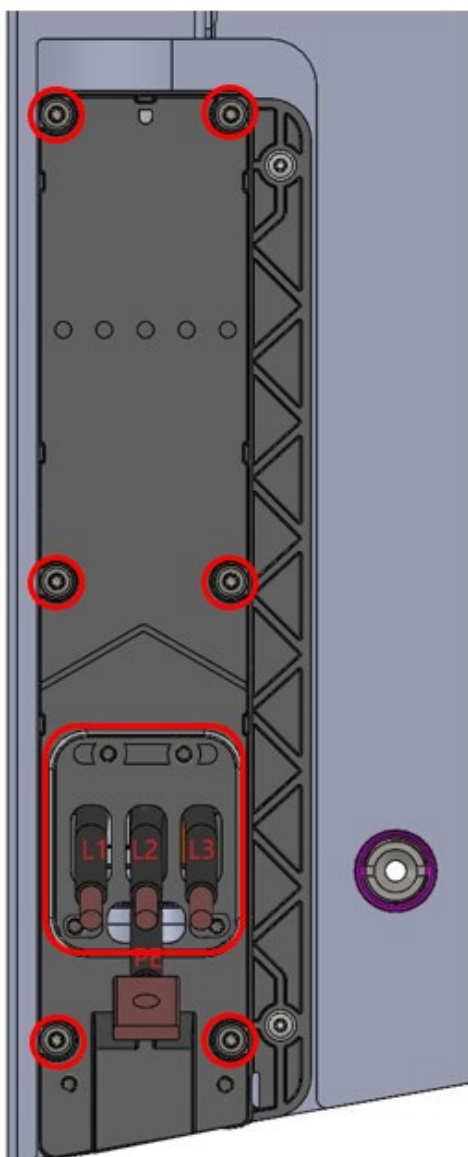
Fasen met kabelbevestiging bevestigen
